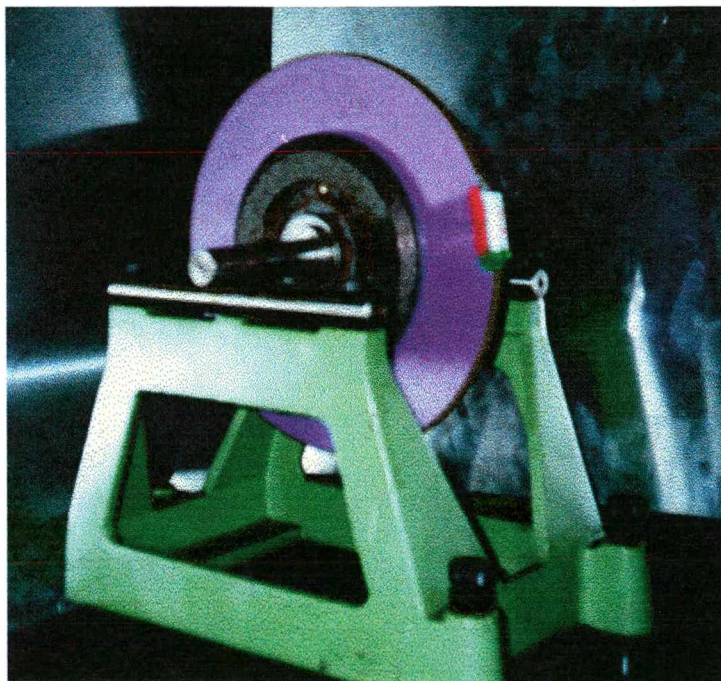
Moldagem da resina flexível numa posição periférica do rebolo
